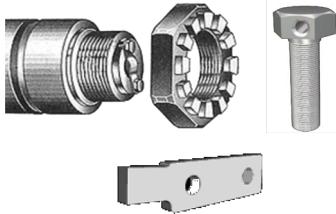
Буксовый узел с двумя подшипниками роликовыми цилиндрическими с торцевым креплением гайкой М110
